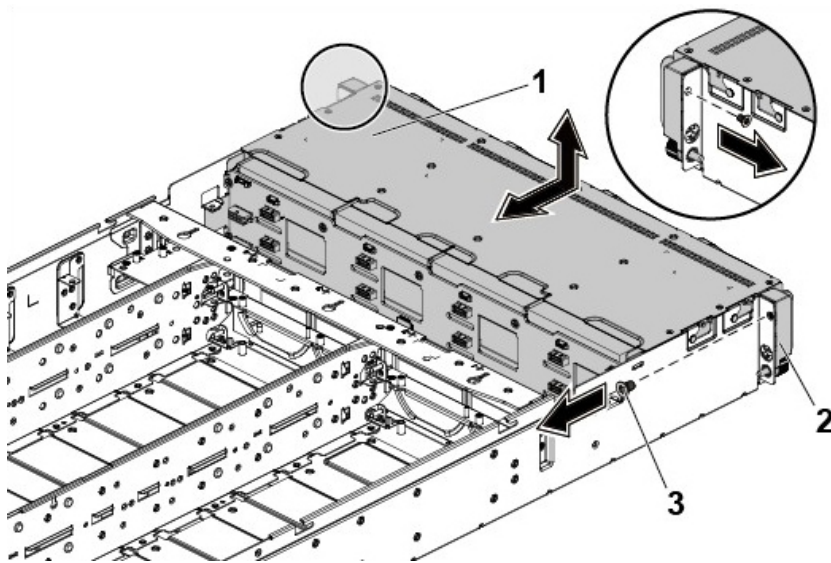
Entfernen und Installieren des Laufwerksgehäuses
